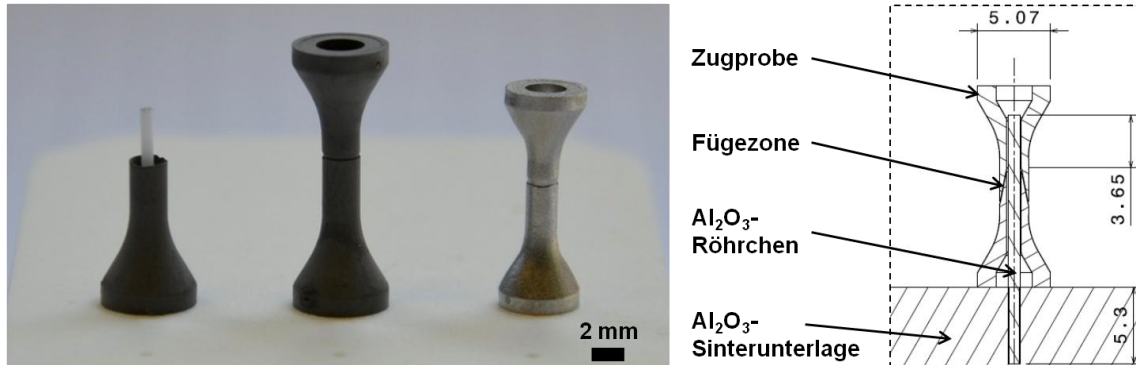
Proben auf modifizierter Sinterunterlage. links: Probenhälfte, grüne Baugruppe und gesinterte Baugruppe; rechts: Ausschnitt aus technischer Zeichnung [Fl-11a]
